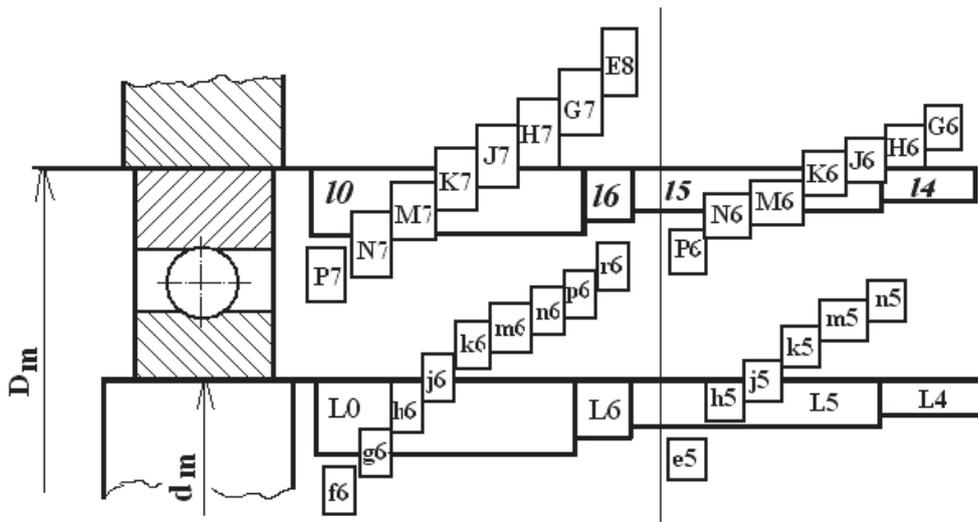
Поля допусков деталей подшипникового соединения
